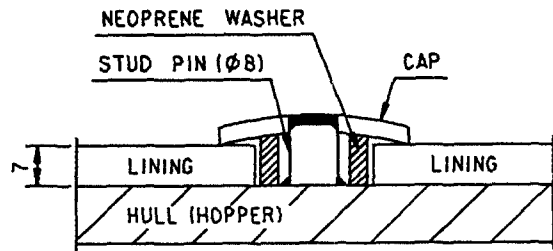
Typical Section of Fastening Element (Lining 표면보다 돌출되어 설치)
